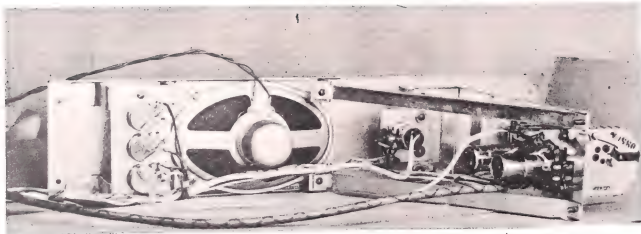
Vista del chasis frontal con el cableado ya conectado
